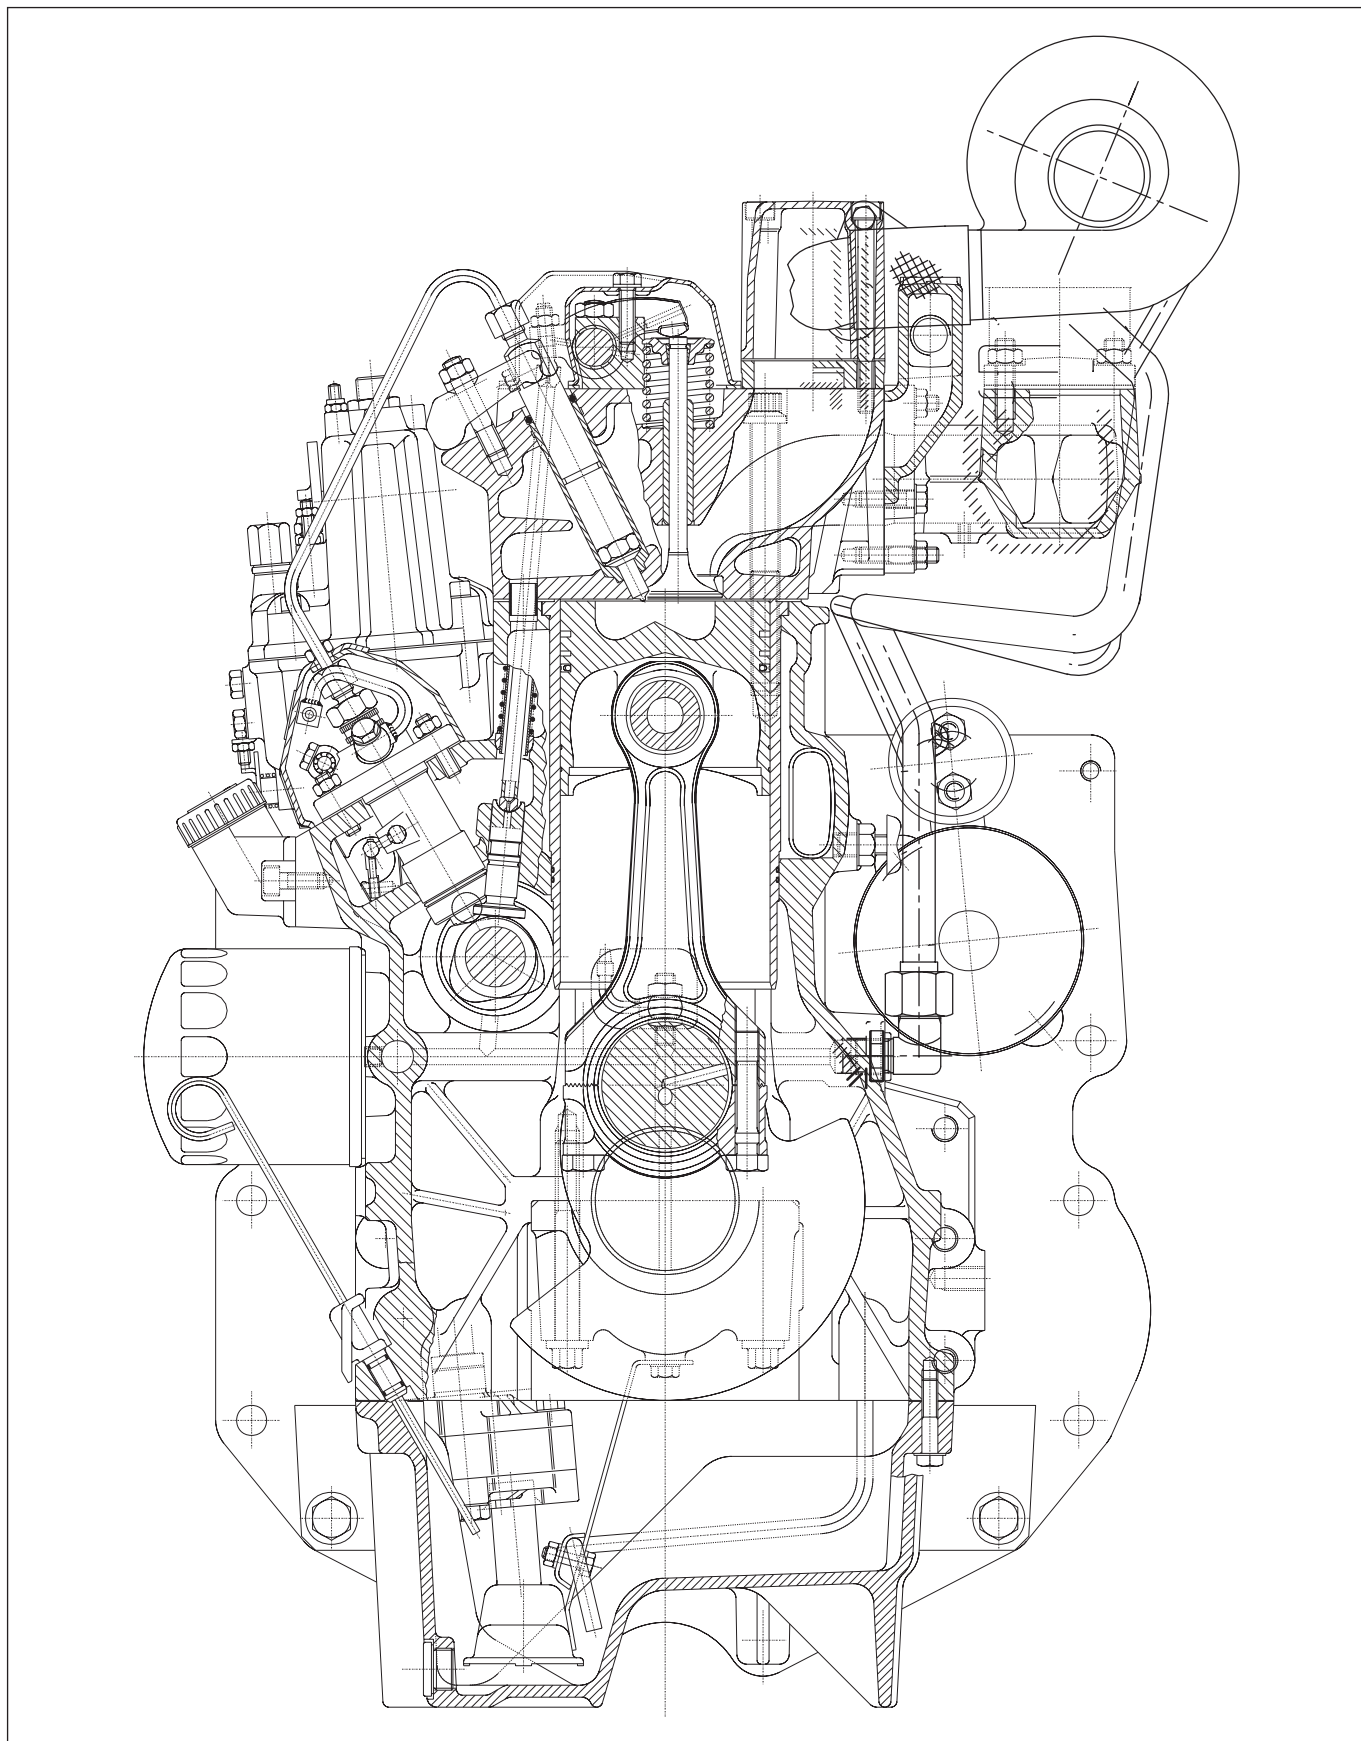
AGROCOMPACT 70F3 - Coupe transversale du moteur - 3 cylindres. TURBO.
